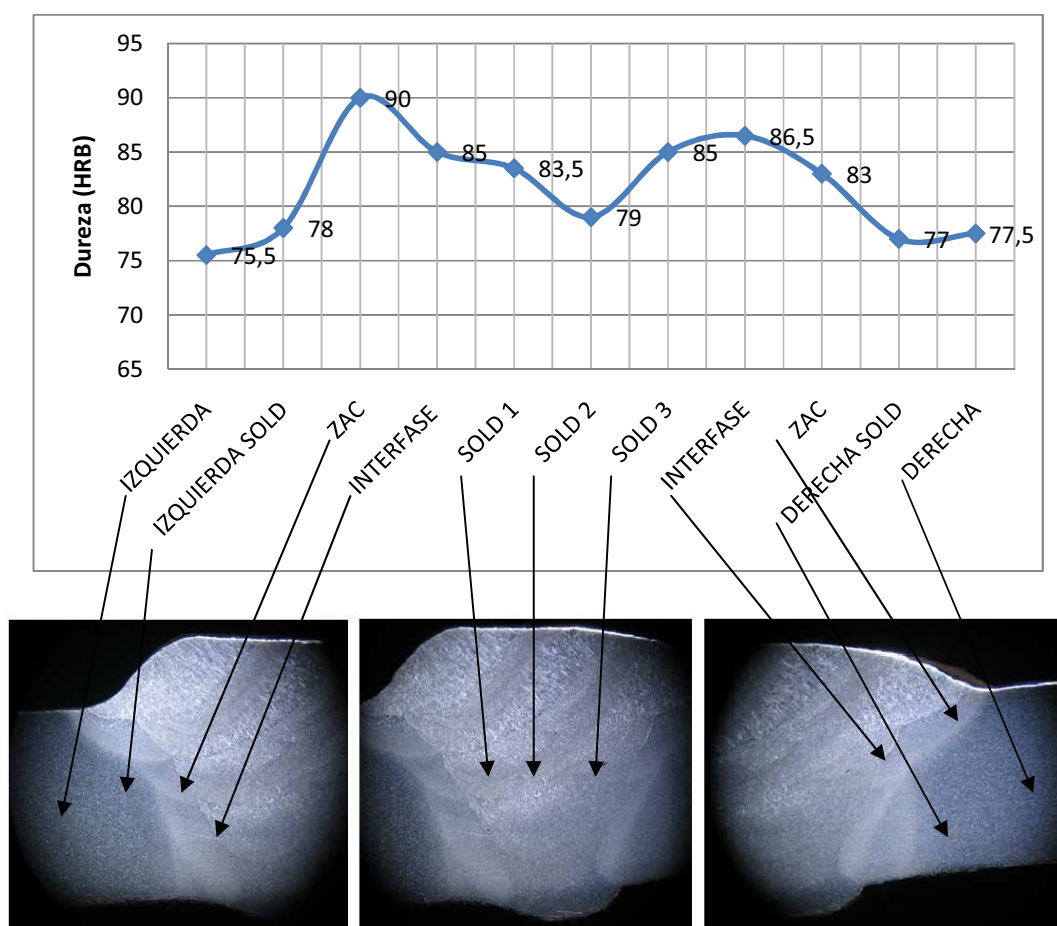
Perfil de durezas en la junta de soldadura sin reparación (10X)
